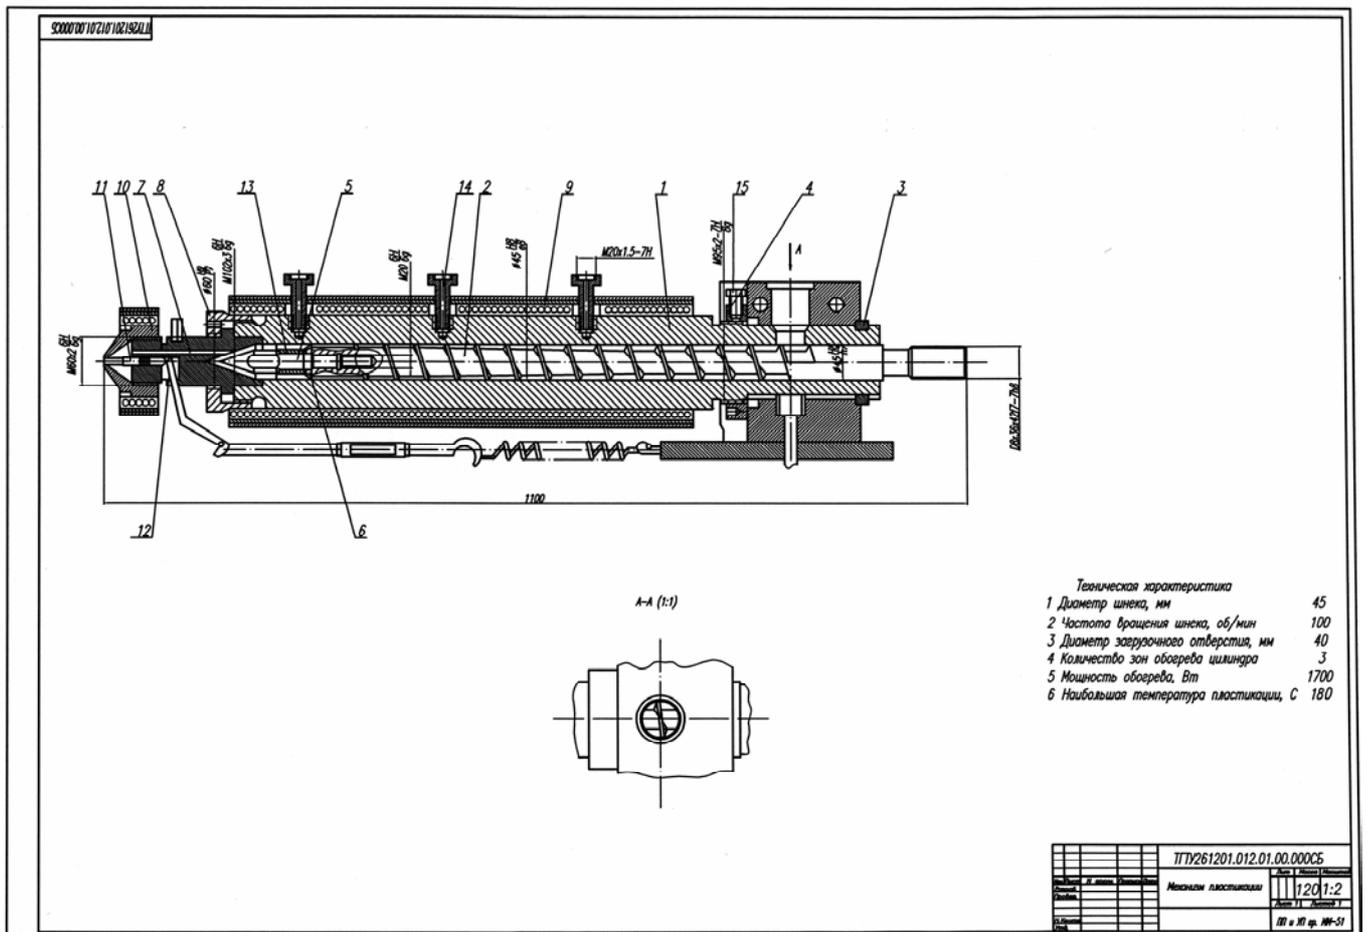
Пример оформления сборочного чертежа пластикационного цилиндра
